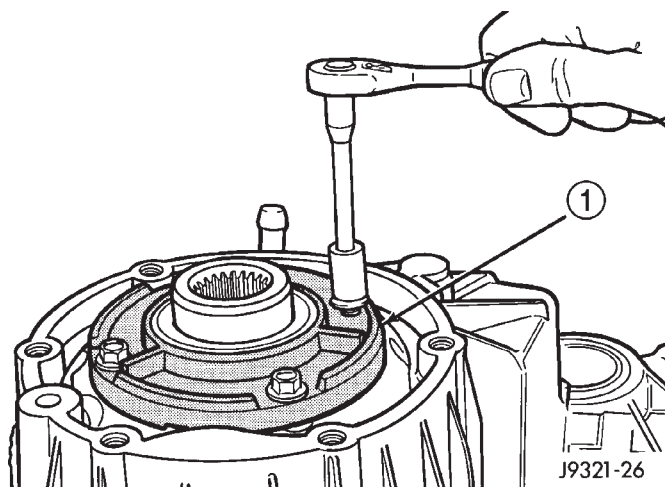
Desmontaje del perno del retenedor del cojinete delantero
